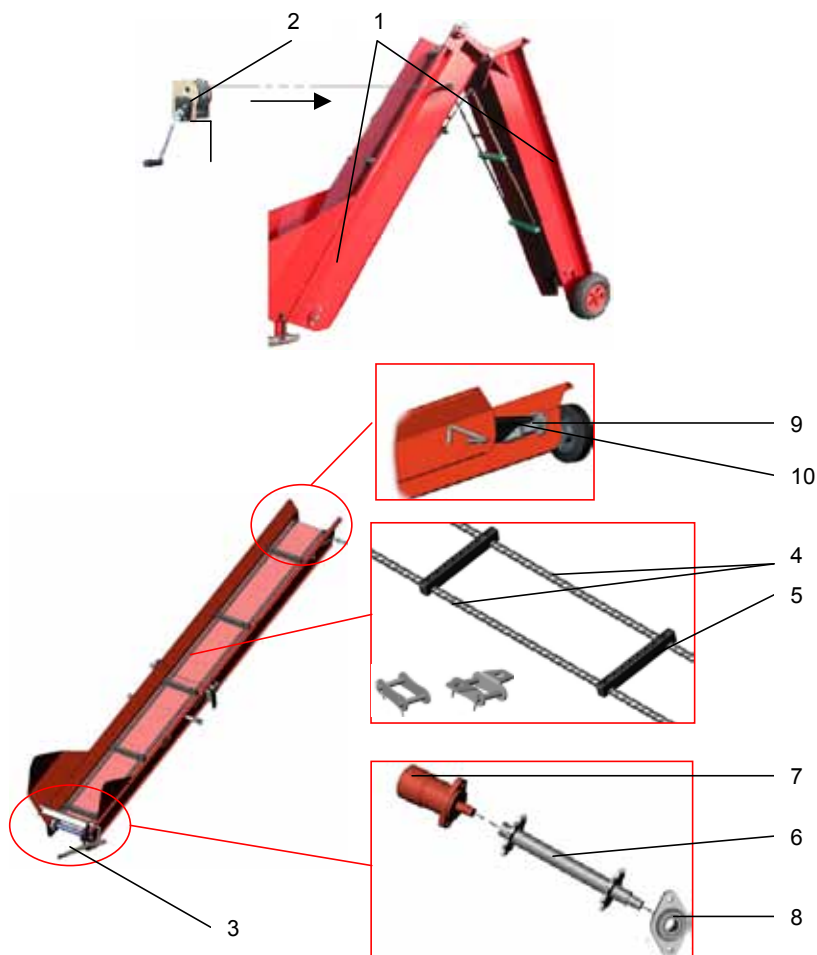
Выводной транспортер Palax Power 100S: 1 – раскладывающаяся рама; 2 – лебедка; 3 – рычаг для фиксации транспортера; 4 – цепи; 5 – скребок (траверса); 6 – вал с ведущими звездочками; 7 – гидромотор; 8 – подшипниковая опора; 9 – звездочка; 10 – механизм натяжения цепи
